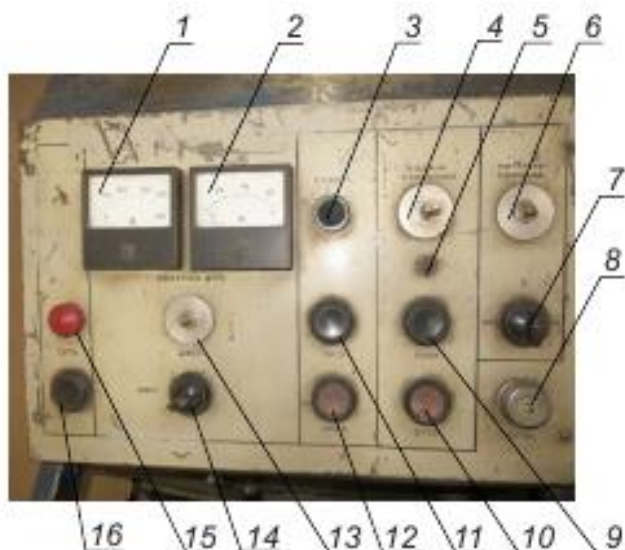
Пульт управления ЭМП-1: 1 – амперметр; 2 – вольтметр; 3 - контрольная лампа "Падение давления воздуха ниже нормы"; 4 - резистор регулирования подачи проволоки; 5 - кнопка пробного включения эл. двигателя металлизатора без сварки; 6 - резистор регулирования частоты колебания механизма порошкового питателя; 7 - включение в рабочий режим порошкового питателя; 8 - кнопка отключения работы металлизатора; 9 и 10 - кнопки пуска и остановка подачи проволоки; 11 и 12 - кнопки включения и отключения сжатого воздуха; 13 - резистор регулирования; 14 - переключатель режима работы (местный или дистанционный); 15 - лампа "Питание в схему подано"; 16 - кнопка включения питания сети.
